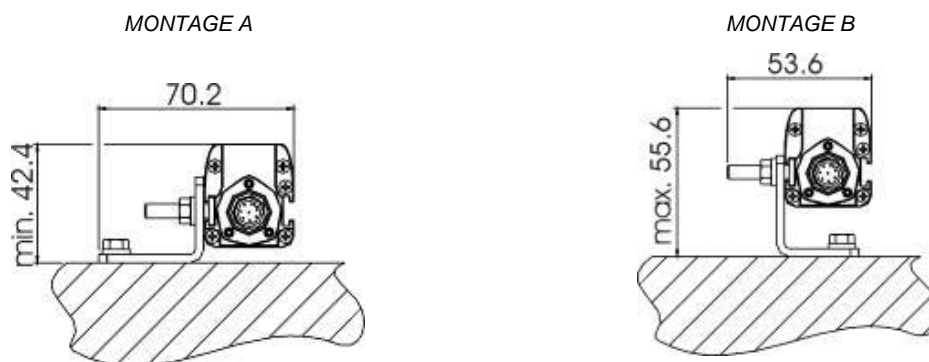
Abmessungen Montagewinkel mit Profil
